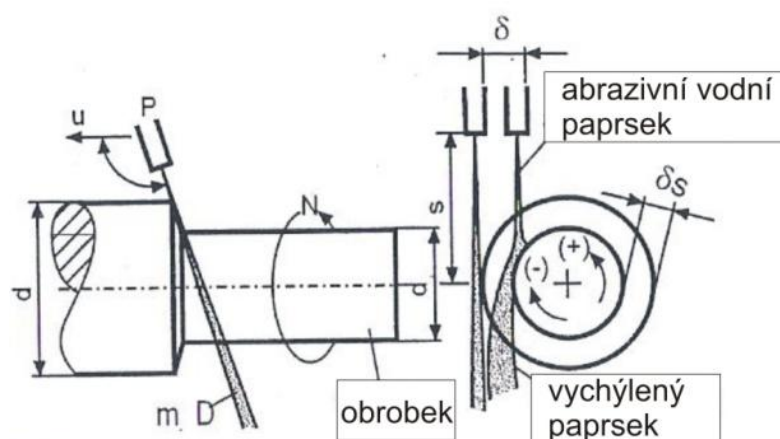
Řezný cyklus při frézování AWJ paprskem⁸.
